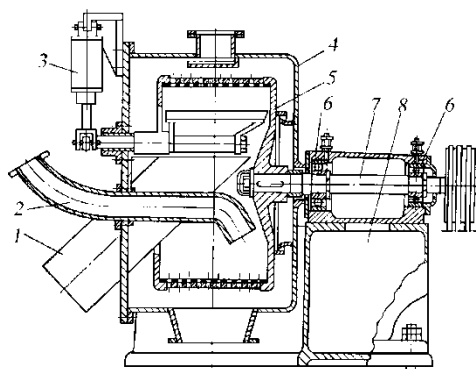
Центрифуга с ножевой выгрузкой осадка и с консольным ротором:
